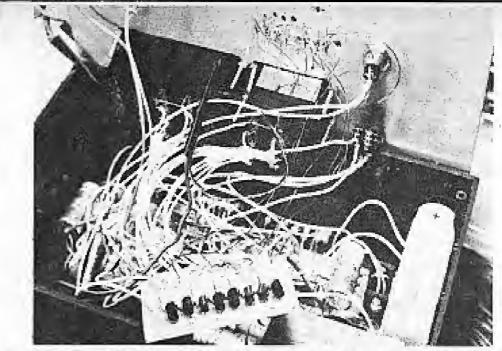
Trois techniques ont été employées pour le câblage : le circuit imprimé (visu-données), le plaquette à trous pour essemblage sens soudure et le wrapping (les LEDS de la visu). Visibles è droite : les deux régulateurs de tension d'alimentation + 5, - 6.
